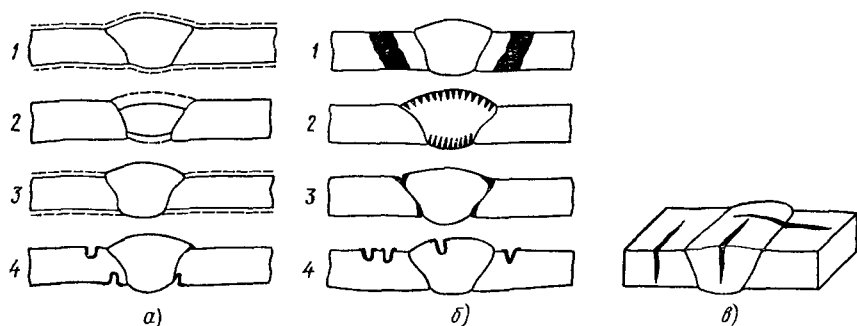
Виды коррозионных разрушений сварных соединений:
